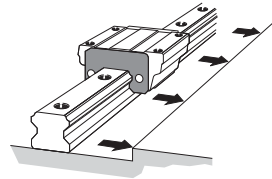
Выравнивание рельса LM относительно базовой поверхности
